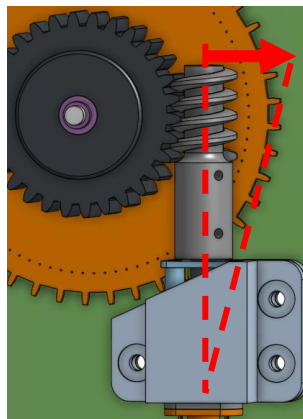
Montierter Sprocket-Antriebsmotor und Getriebe
